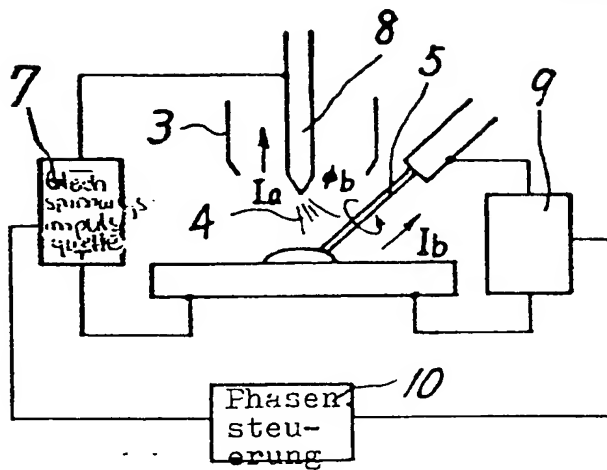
(b) Impulsquelle für Schweißdraht
